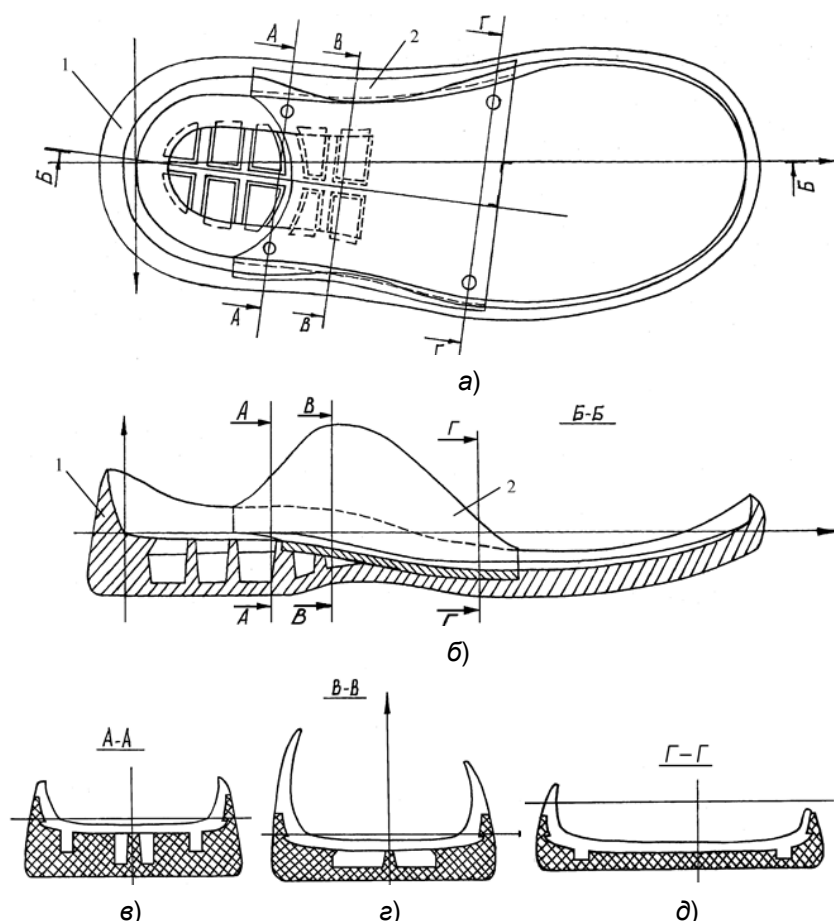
Конструкция модифицируемой ортопедической подошвы со сменным вкладышем: а – вид с неходовой стороны, б – продольно-осевое сечение, в-д – поперечно-вертикальные сечения
